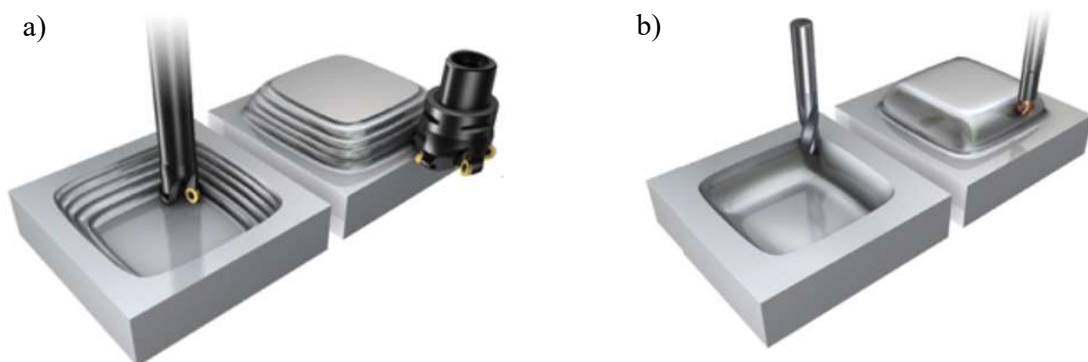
a) čelní frézování b) vysoko posuvové frézování [17]
